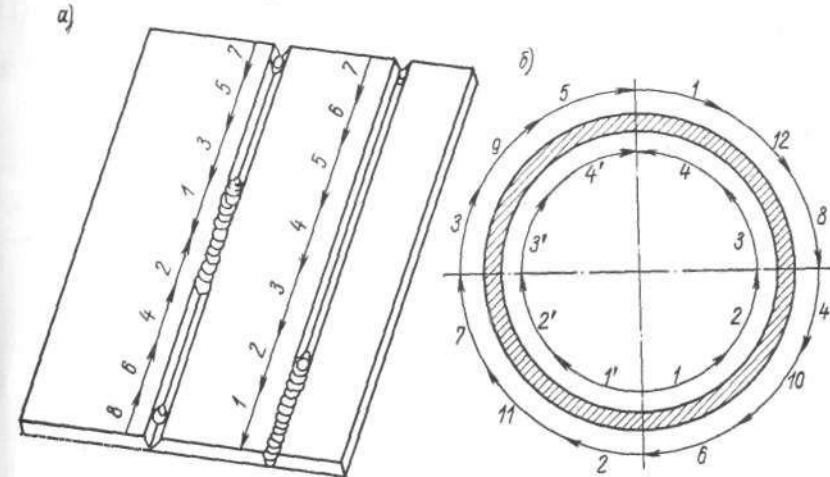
Последовательность наложения швов: а — при сварке плоскостных конструкций; б — при сварке кольцевых соединений.
